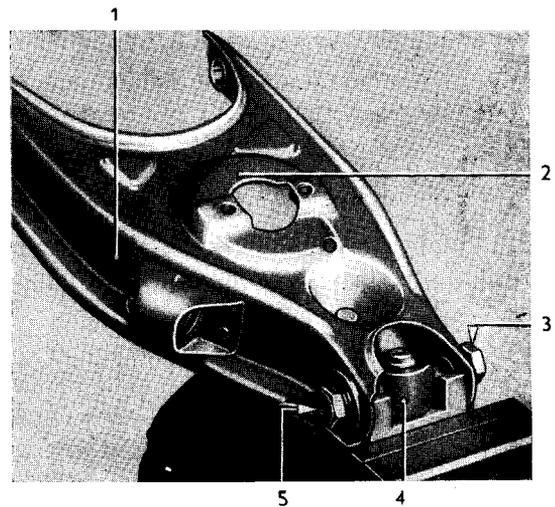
Lenker mit Querstück auf Vorspannstück aufgesetzt
